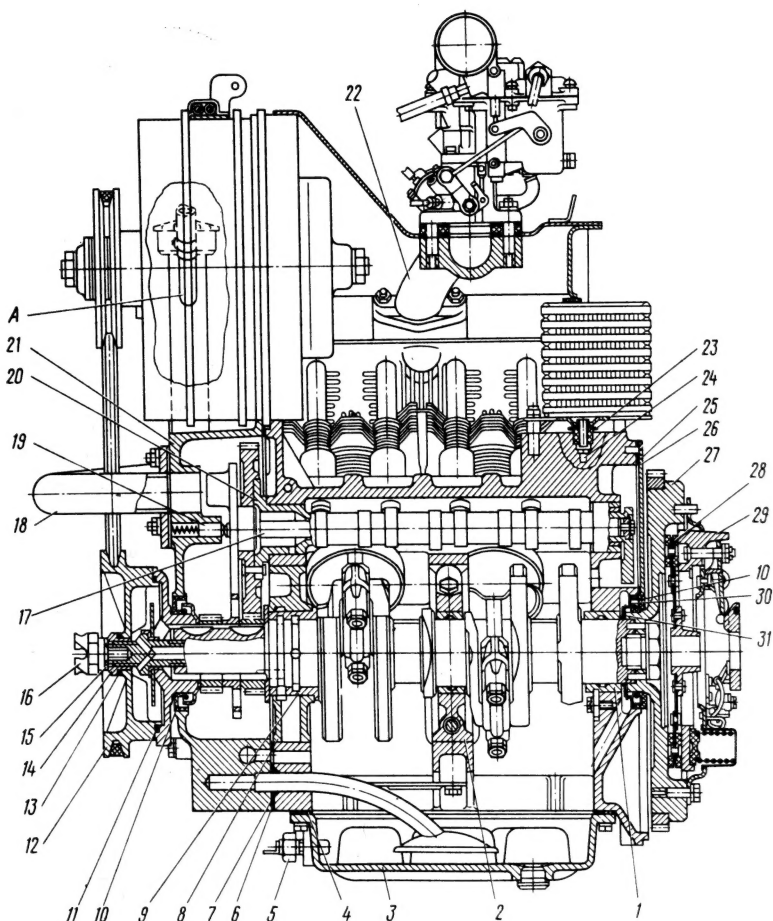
Продольный разрез двигателя MeMZ-966Г:
